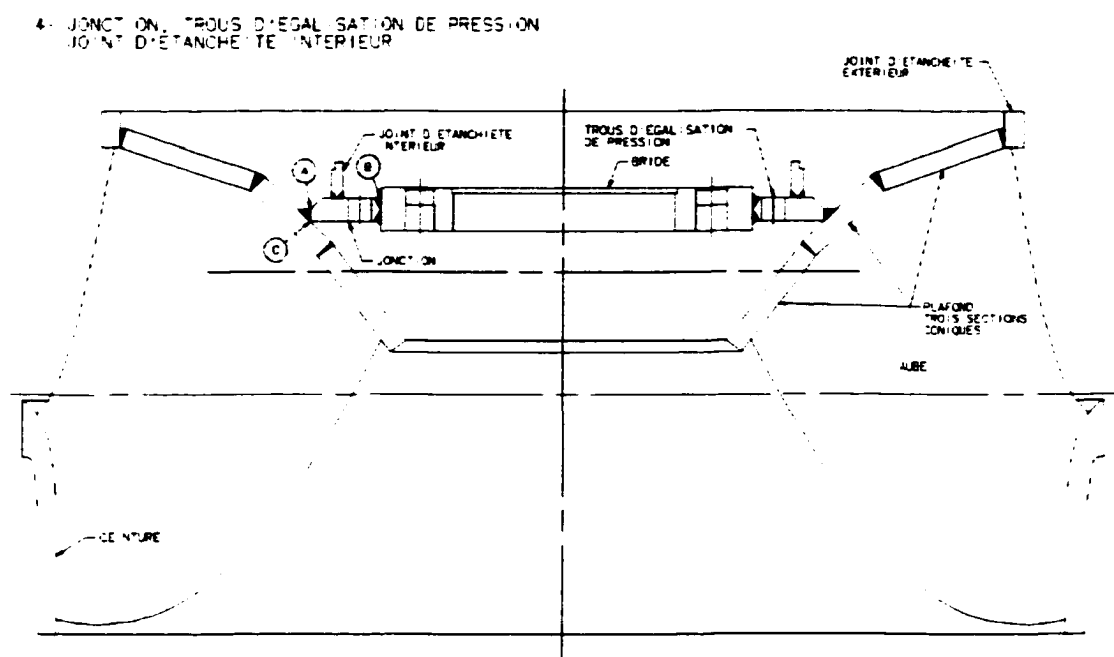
Couronne mécano-soudée en acier ASTM A240 UNS 30403
